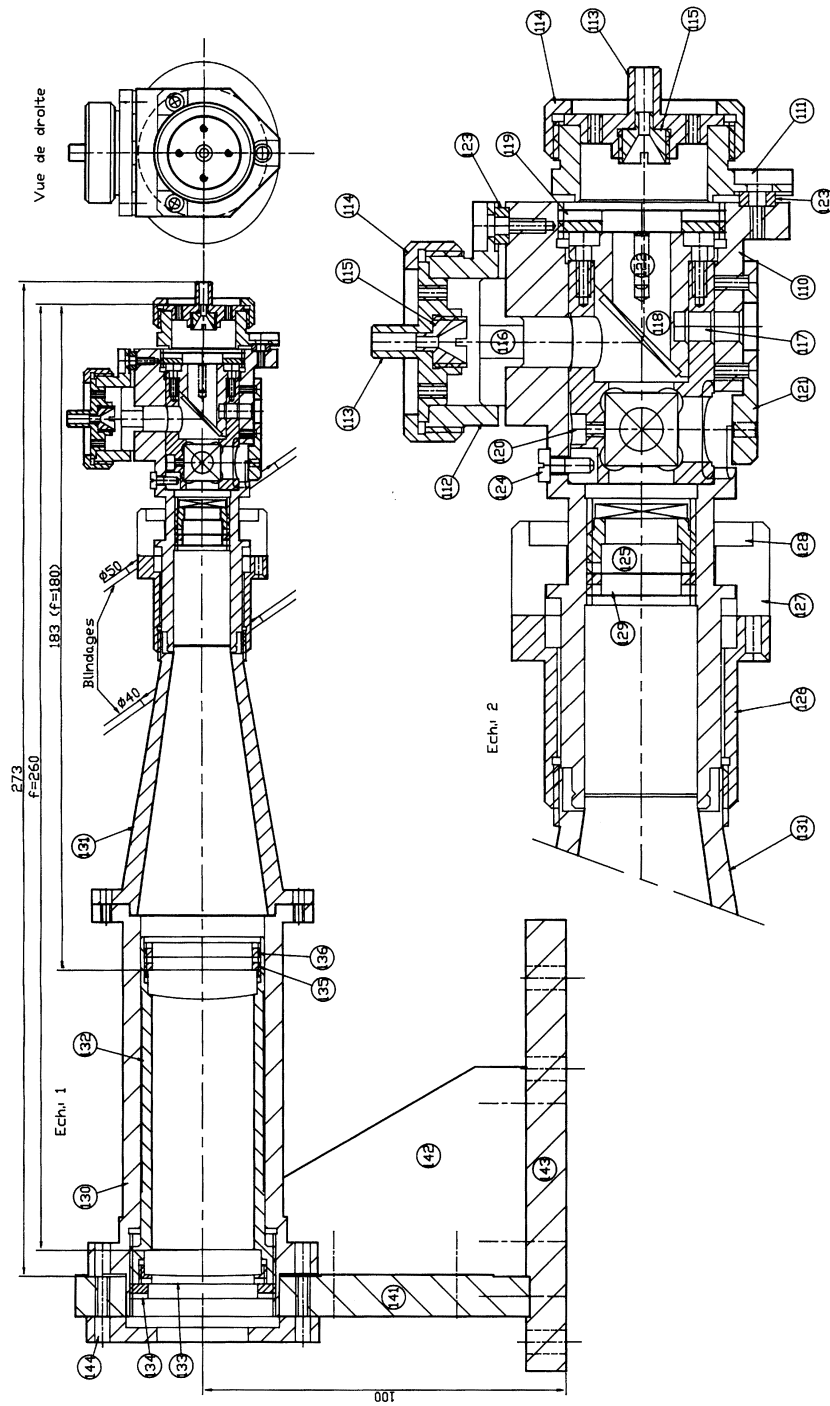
Coupes du collimateur dichroïque prototype.
